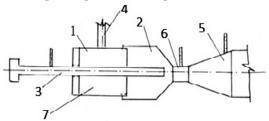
Принципиальная схема охлаждающего эжектора: 1-цилиндрический корпус; 2 - конфузорный корпус; 3 - сопло; 4 - водоподводящий патрубок; 5 - диффузорсмеситель; 6 - цилиндрическая муфта; 7- полость корпуса
